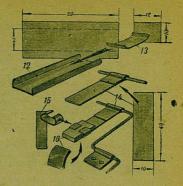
Детали перфоратора: желобок, козырек и части подающей и тормозной пластинок.
